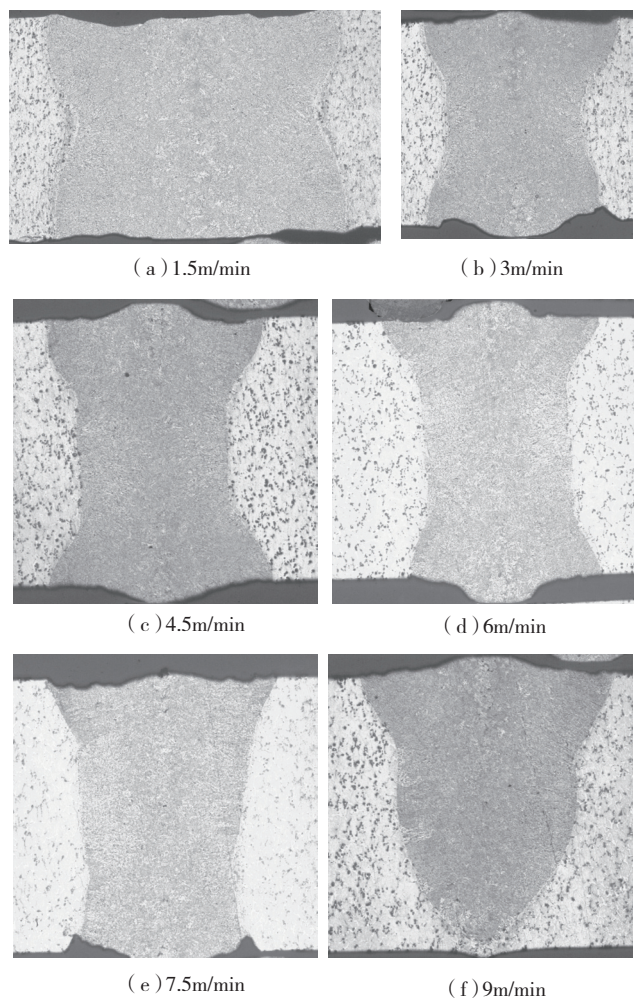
焊接速度对光纤焊缝横截面形貌的影响
